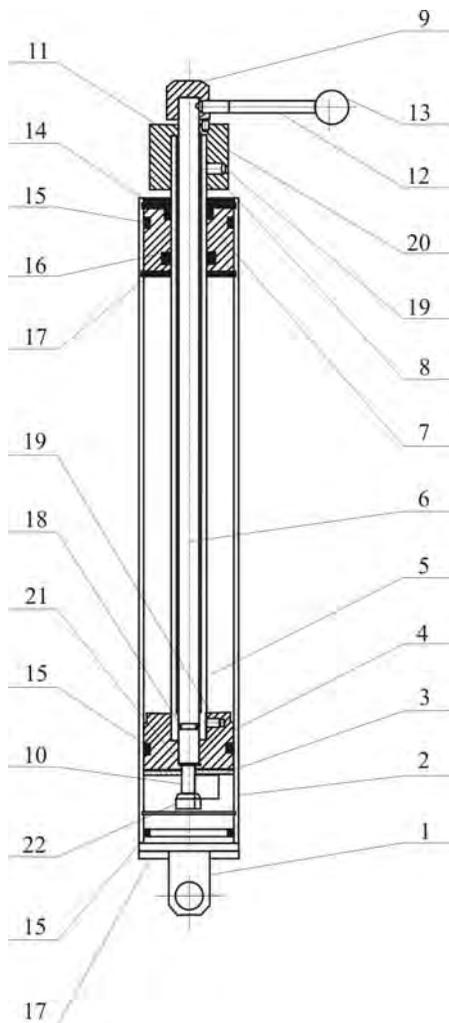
Цилиндр рамы пилы станка модели 230G в сборе:
